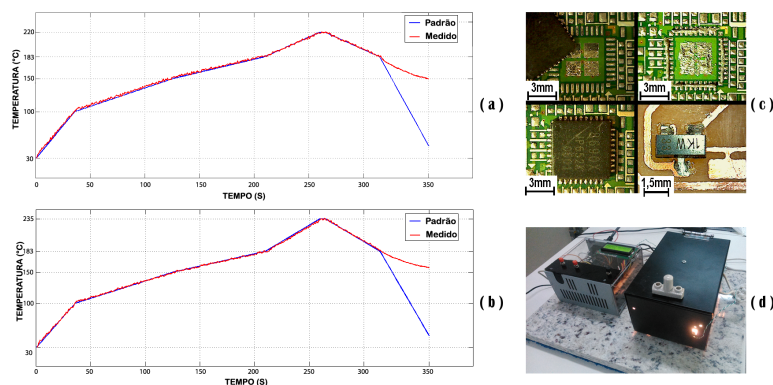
(a) Curvas de 220°C; (b) de 235°C; (c) placa com componentes soldados e (d) forno construído.
